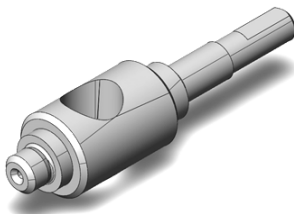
Схема базирования заготовки на фрезерной операции
